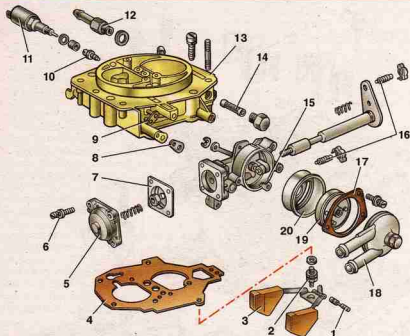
Детали крышки карбюратора 21083—110710-31: 1 — ось поплавка; 2 — игельчатый клапан; 3 — поплавок; 4 — прокладка крышки карбюратора; 5 — крышка пускового устройства; 6 — винт; 7 — диафрагма пускового устройства; 8 — прокладка; 9 — рычаг воздушной заслонки; 10 — топливный жиклер холостого хода; 11 — электромагнитный запорный клапан; 12 — патрубок подачи топлива; 13 — крышка карбюратора; 14 — топливный фильтр; 15 — корпус полуавтоматического пускового устройства в сборе с рычагами привода; 16 — регулировочные винты пускового зазора воздушной заслонки и притягивания дроссельной заслонки первой камеры; 17 — хомут крепления корпуса биметаллической пружины; 18 — жидкостная камера; 19 — корпус с биметаллической пружиной в сборе; 20 — экран биметаллической пружины
